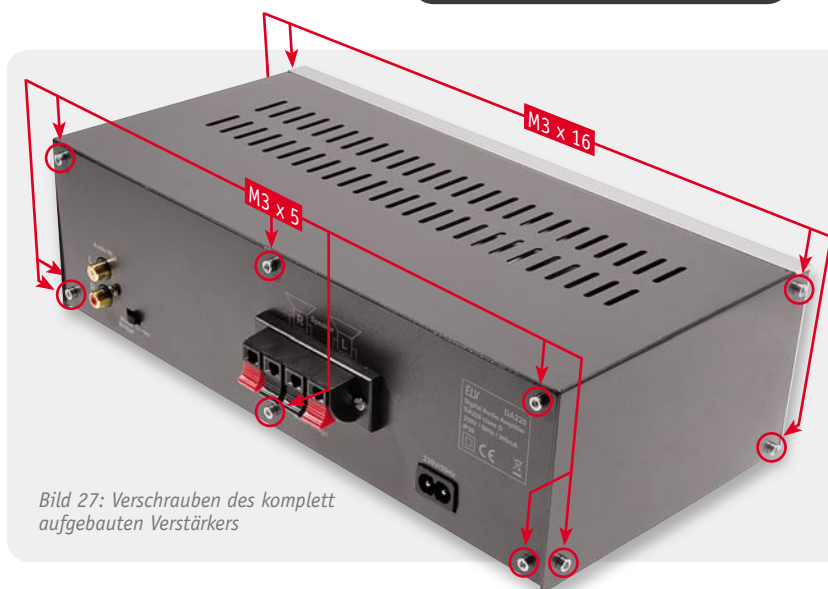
Verschrauben des komplett aufgebauten Verstärkers
